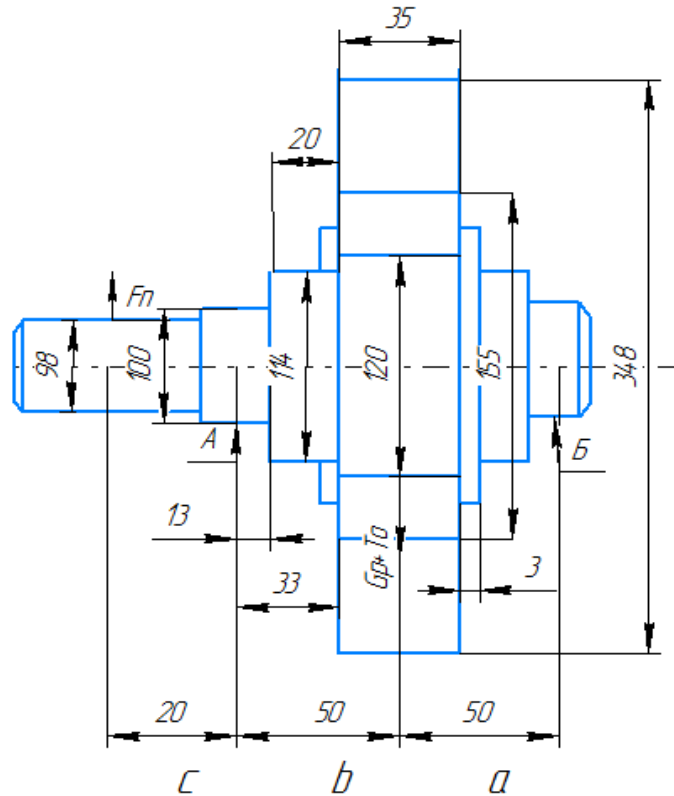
Эскиз вала с размерами и обозначением опор.
